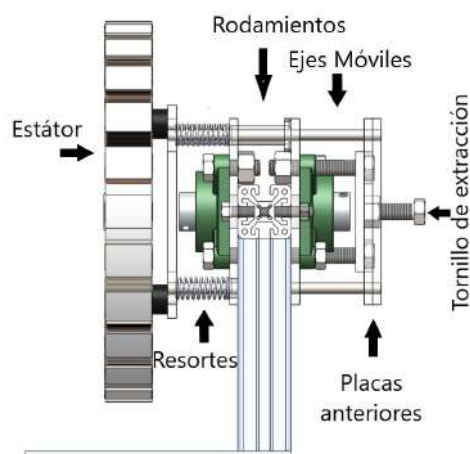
Ensamblaje del mecanismo de extracción con estátor.
